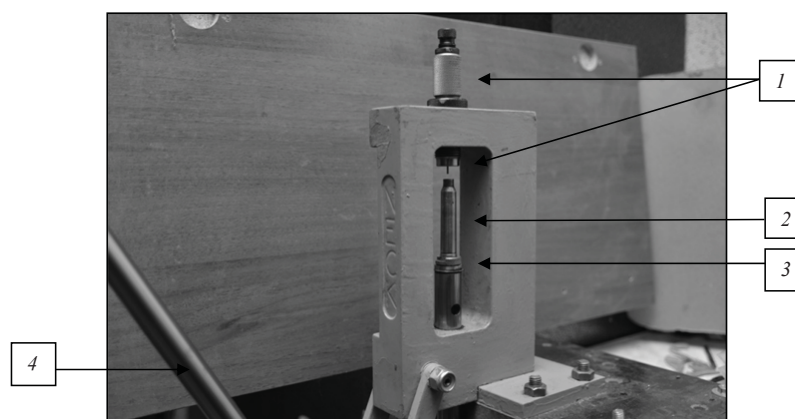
Вид прессы, подготовленной к переснаряжению гильзы: 1 – формовочная матрица, 2 – гильза, 3 – гильзодержатель (шеллхолдер), 4 – шток прессы
